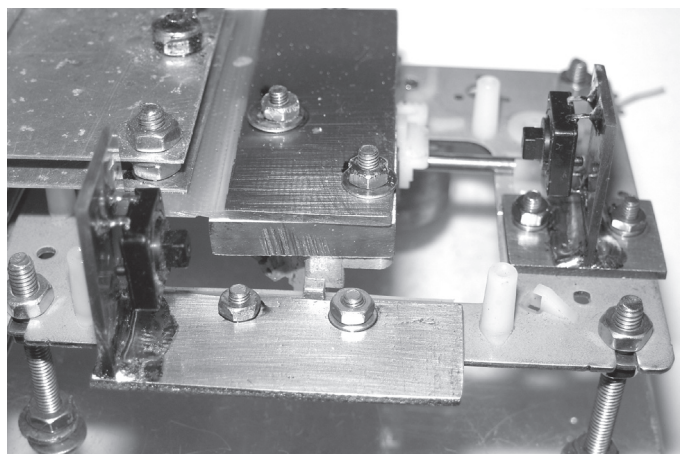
Détail des plaques mobiles. Au centre, une plaque hardboard de 5 mm d'épaisseur et de 20 x 30 mm, fixée sur la pièce d'alu mobile et du circuit imprimé de 40 x 50 mm par deux vis et écrous de 3 mm. A gauche: les deux plaques d'aluminium vissées sur sur le circuit imprimé époxy double face. Attention: les plaques d'aluminium sont isolées par rapport au châssis du mécanisme (espacées par des écrous de 4 mm). En bas à gauche et au centre à droite, les deux interrupteurs de fin de course. Pour toute clarté, les tampons qui doivent activer les interrupteurs ne sont pas encore montés.
